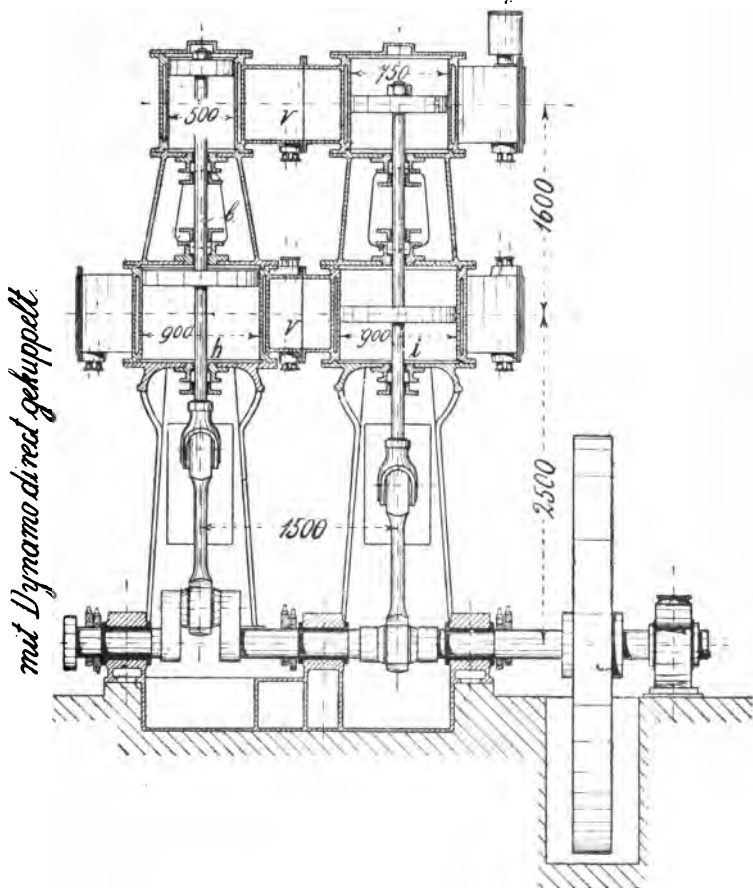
Dreifach-Expansionsmaschine. Masstab 1:40.
